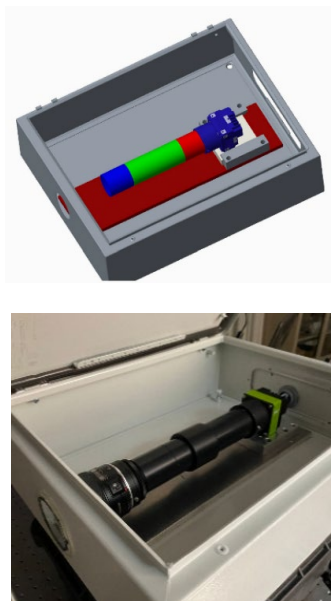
(Arriba) Diseño mecánico de la cámara polarimétrica. (Abajo) Fotografía de la cámara polarimétrica montada.
